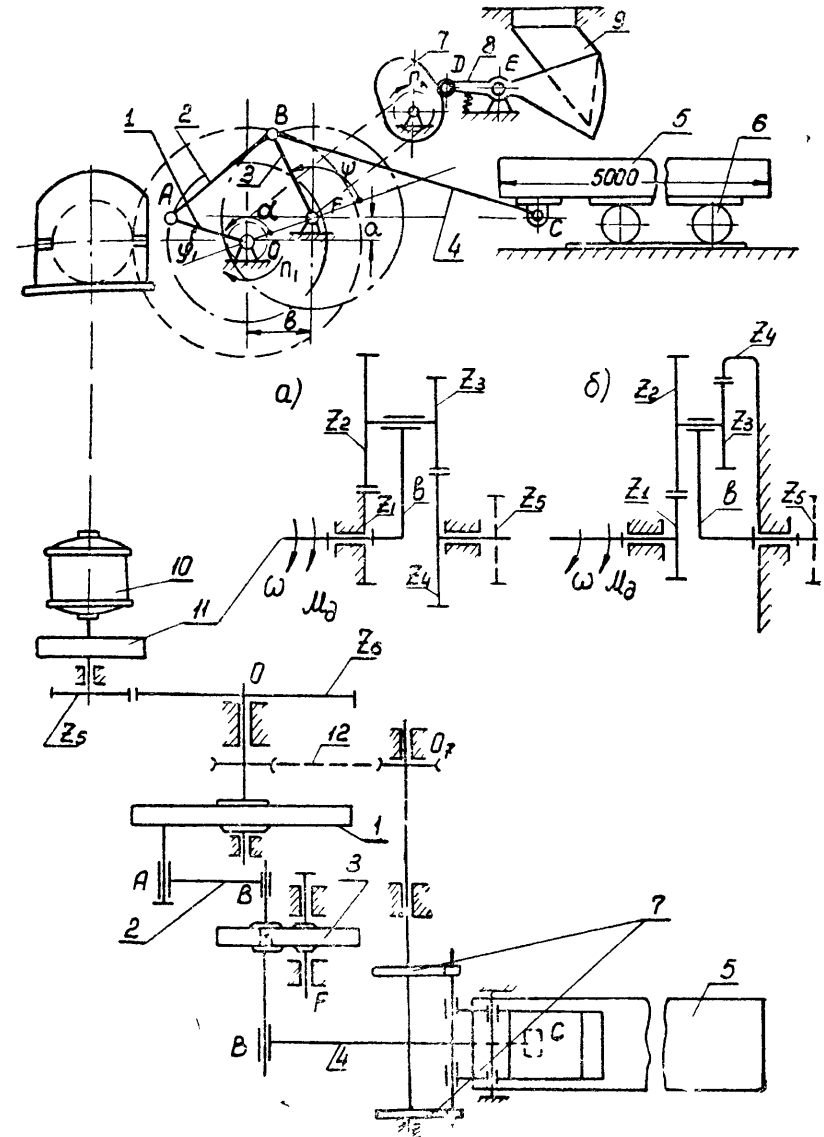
1. Схема механизмов качающегося конвейера и схема планетарного редуктора
